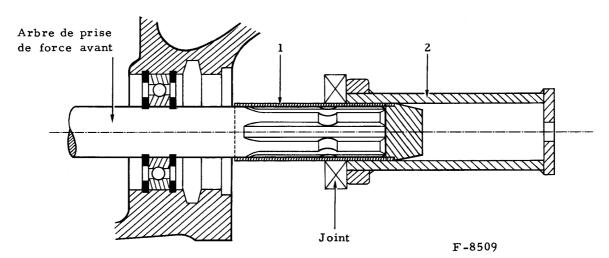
Montage du joint d'étanchéité de la prise de force avant.
